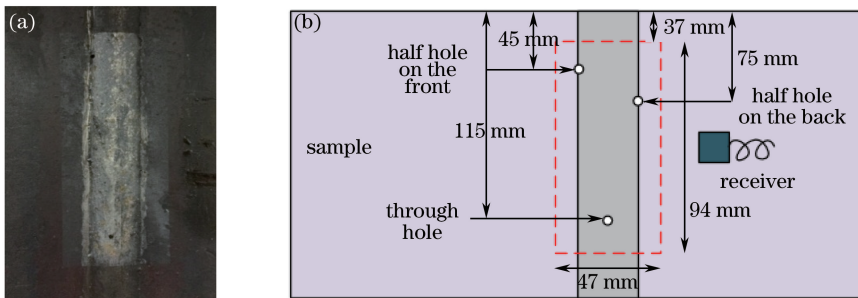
具有模拟缺陷和扫描面积的焊接试验样品。(a)实物图;(b)尺寸
